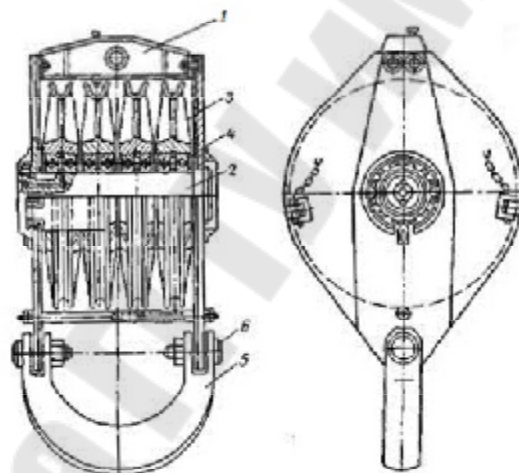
Талевый блок: 1- полая траверса; 2- ось; 3-шкивы; 4- подшипники качения; 5- серьга; 6- съемный палец
